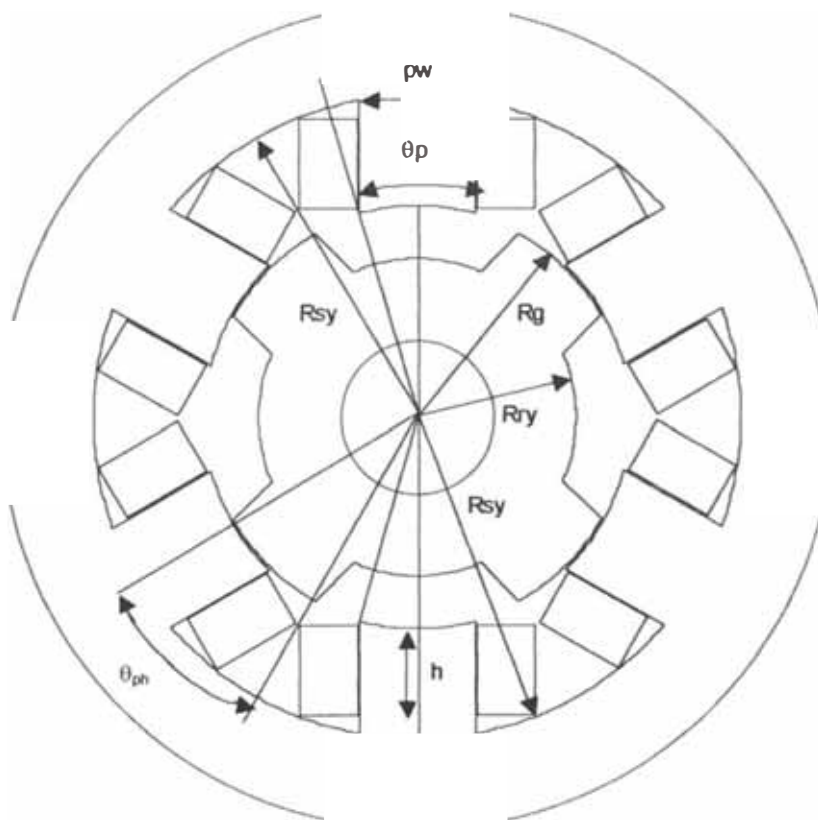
Corte seccional de un motor de reluctancia, (dimensiones)
